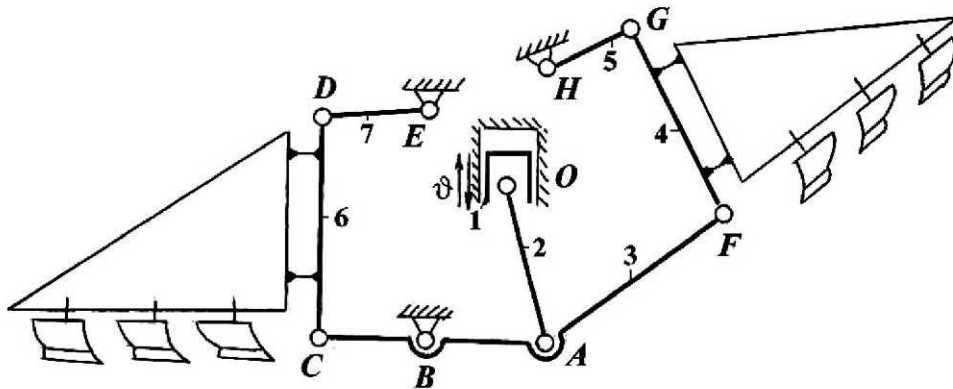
Механизм навески плугов для гладкой пахоты (челночный плуг)
